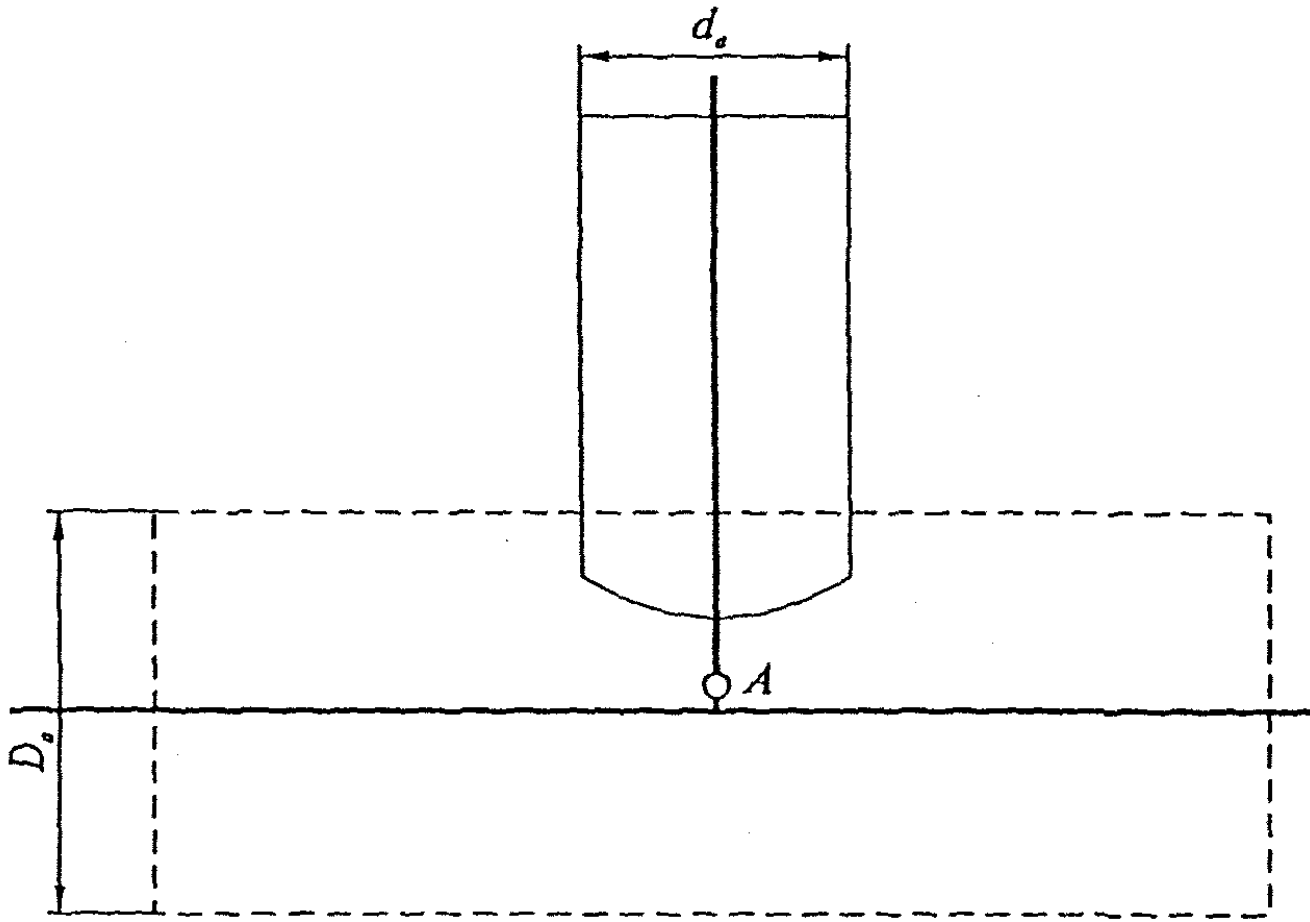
Расчетная схема Т-образного сварного соединения трубопровода
